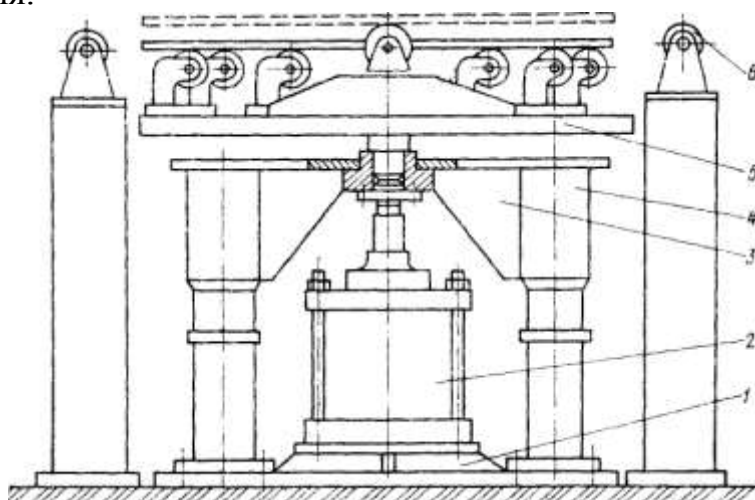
Подъемно-поворотный стол: 1 — основание; 2 — пневматический подъемник; 3 — основание стола; 4 — колонна направляющая; 5 — стол поворотный; 6 — рольганг
